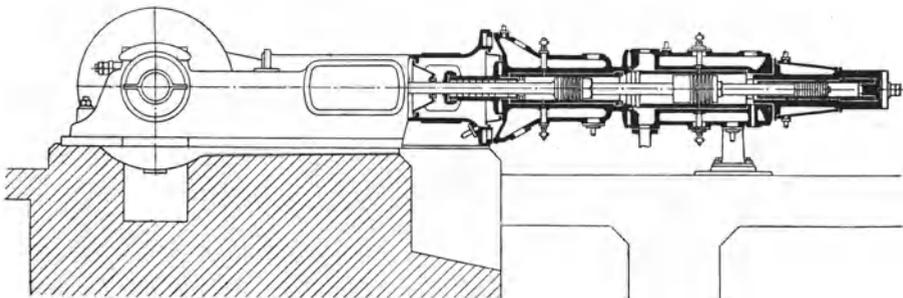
Sechsstufiger Gaskompressor, Höchstdruckseite (Gebr. Sulzer).
